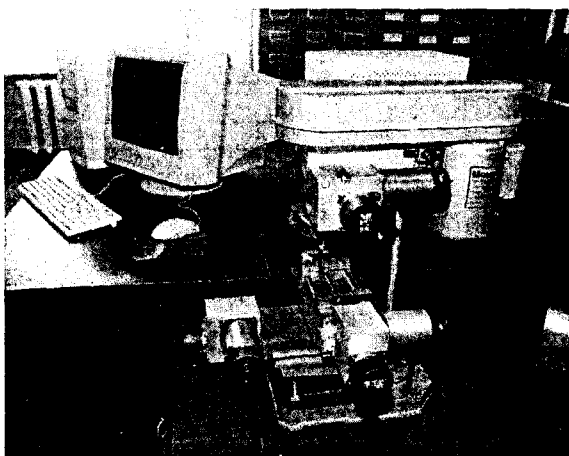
Учебный сверильно-фрезерный станок с ЧПУ
